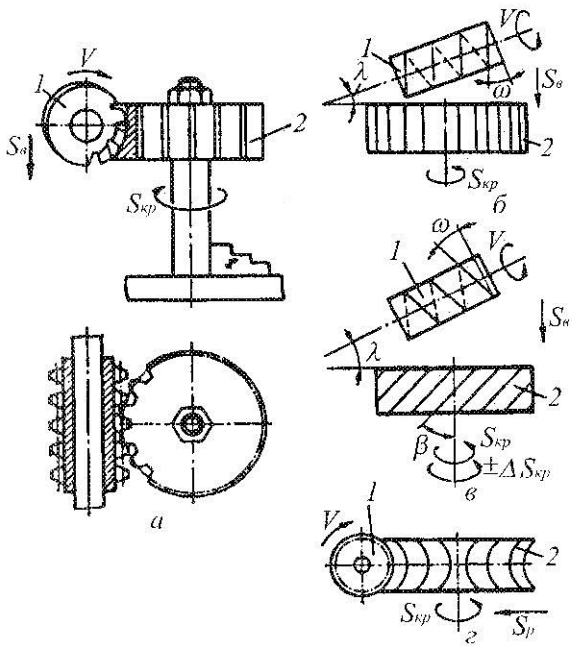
Схеми нарізування циліндричних зубчастих коліс на зубофрезерному верстаті
